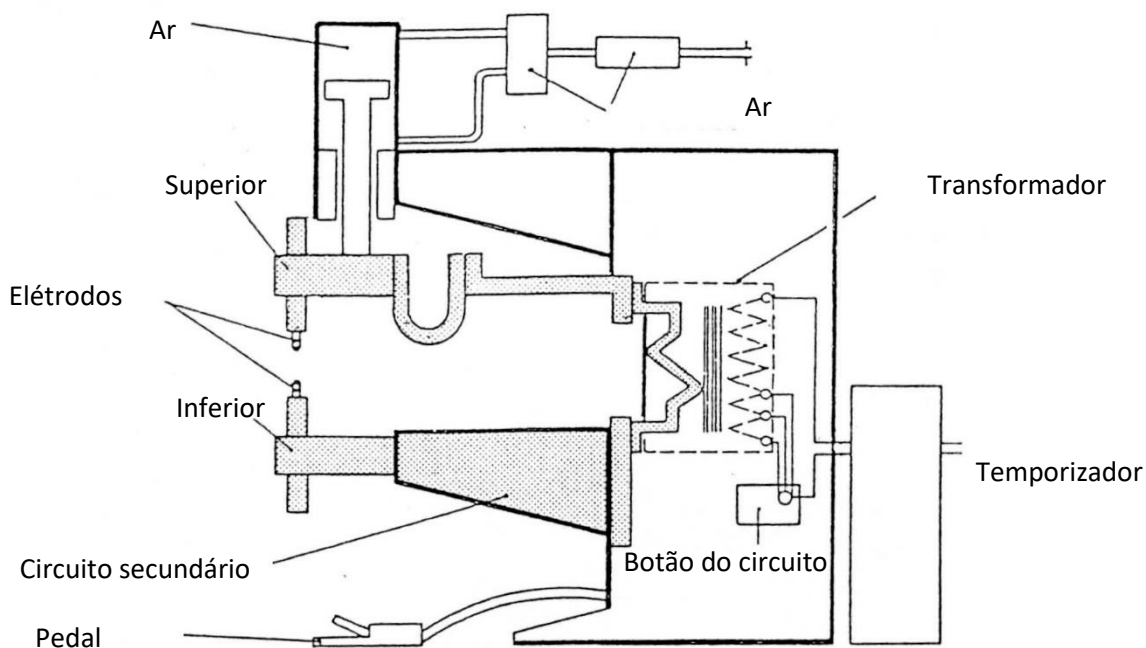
Máquina de solda a ponto com pedal. Fonte: TWI
